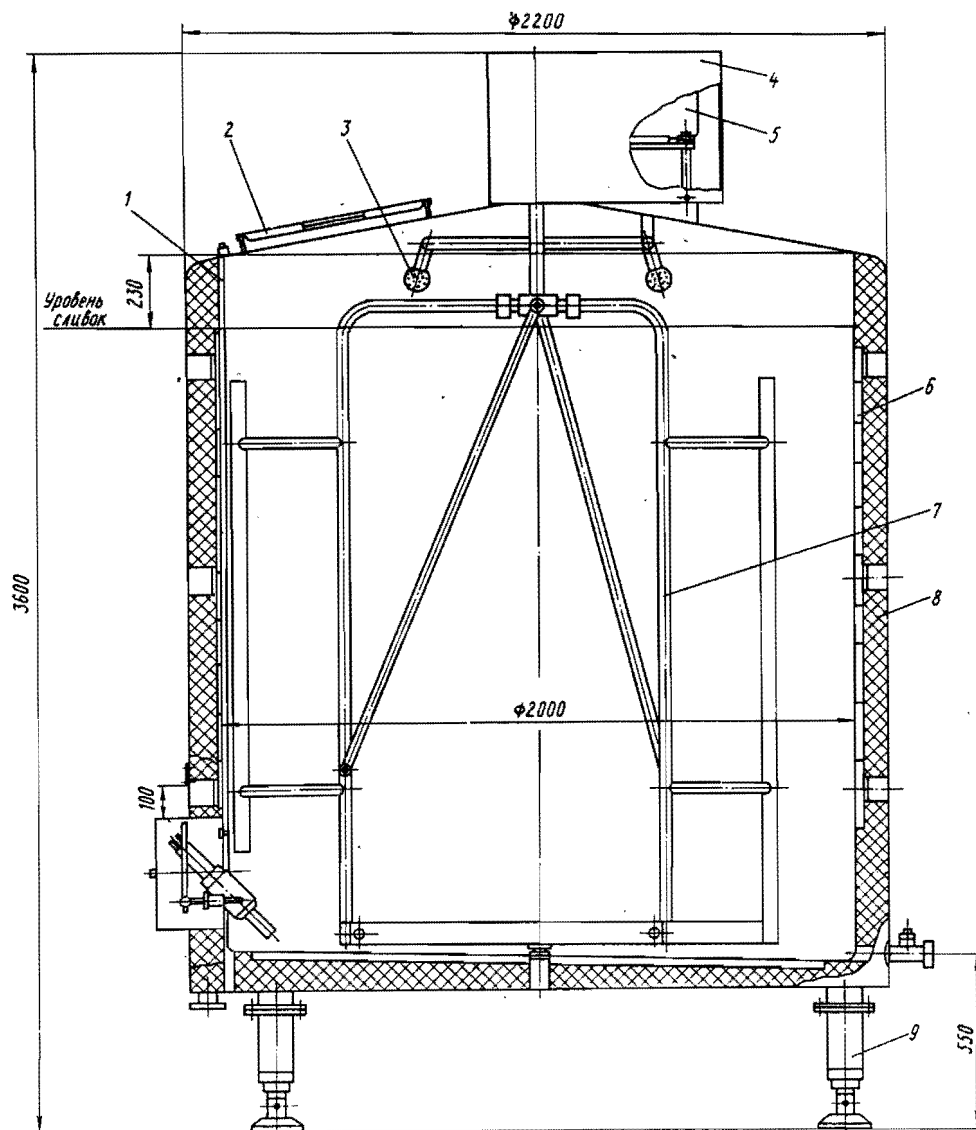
Общий вид (разрез) резервуара сливок-созревателя марки Л5-ОТН-6300:
